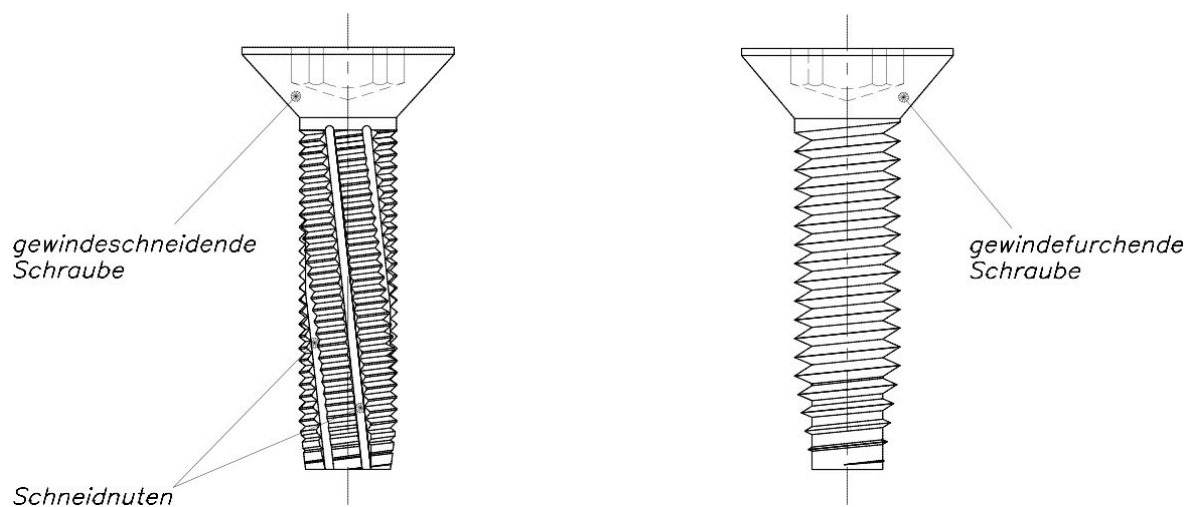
Gewindeschneidende und gewindefurchende Schrauben
